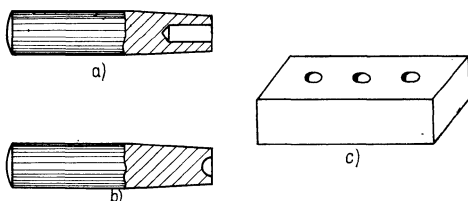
Nietwerkzeuge; Nietzieher (a), Nietkopfschneider (b) und Gegenhalter (c) zum Einspannen in den Schraubstock
